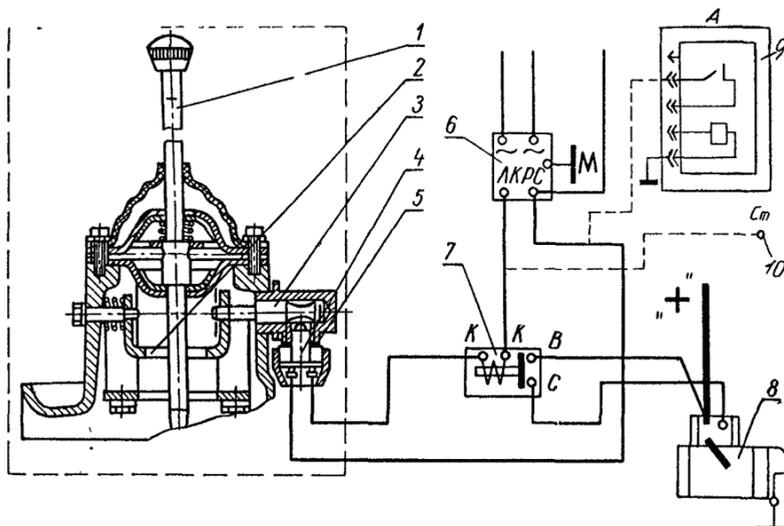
Схема блокировки запуска дизеля Д-243. 1 — рычаг КП; 2 — рамка; 3 — валик рамки; 4 — выключатель ВК-403; 5 — регулировочные прокладки; 6 — реле блокировки РБ-1; 7 — реле стартера; 8 — стартер; 9 — реле 111-3747; 10 — клемма "Ст" выключателя стартера; А — вариант для трактора с унифицированной кабиной
